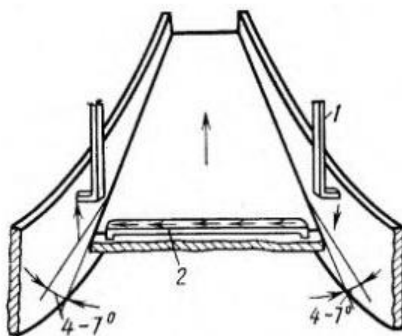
Схема подвода тока в зону сварки
